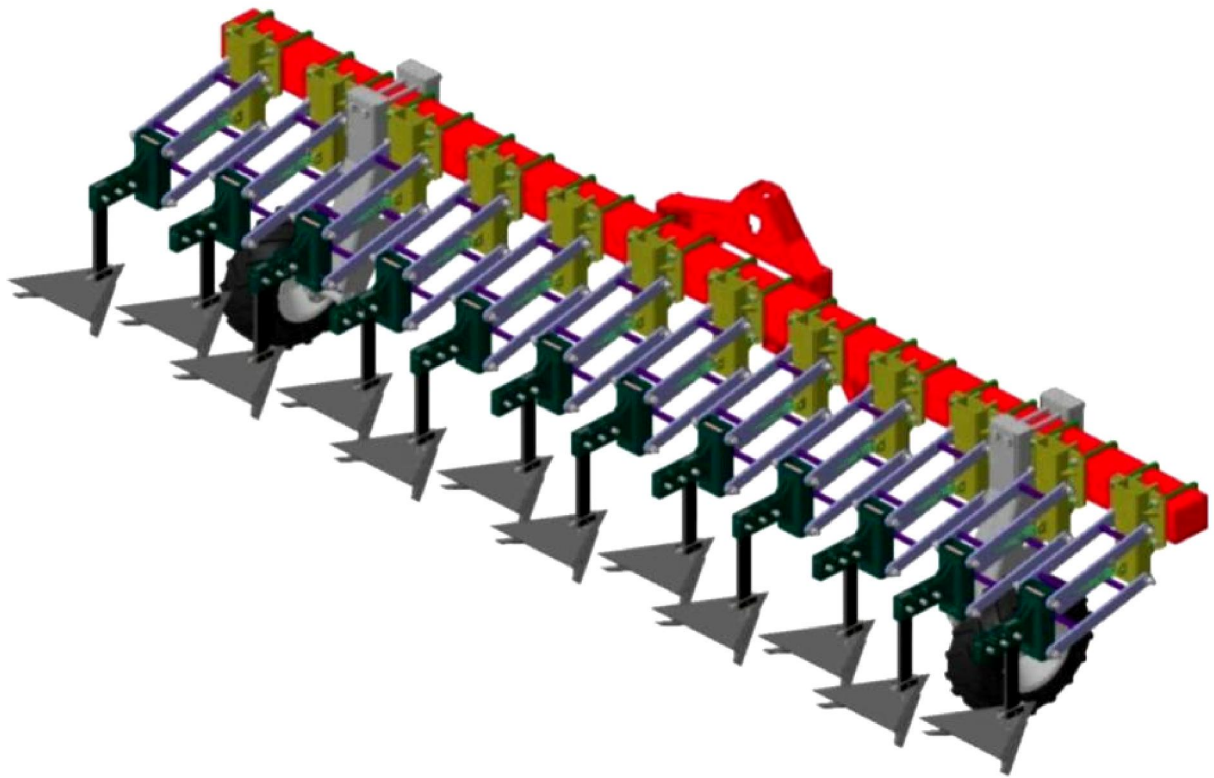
Загальний вид культиватора з двохранними стрілочастими лапами
